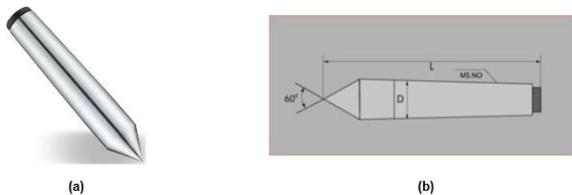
(a) Ponto fixo, (b) Desenho técnico (Anon., 2014)
